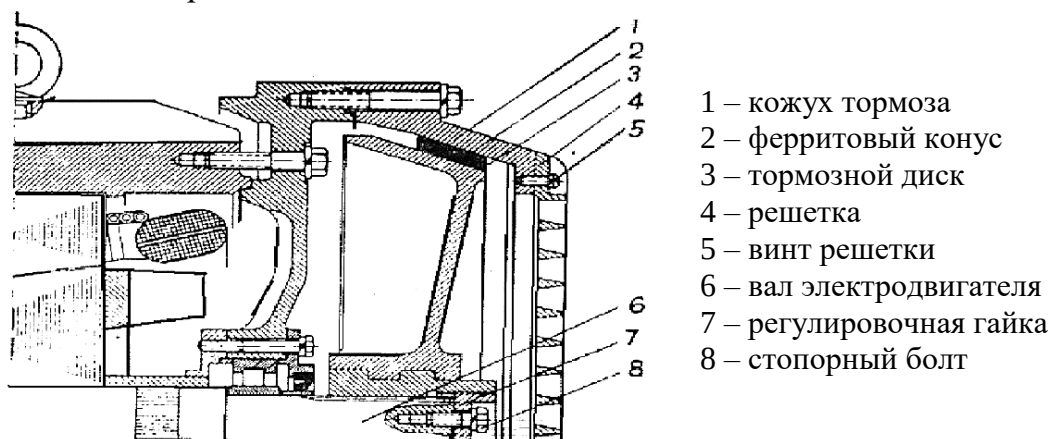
Частичный разрез электродвигателя подъемного механизма
